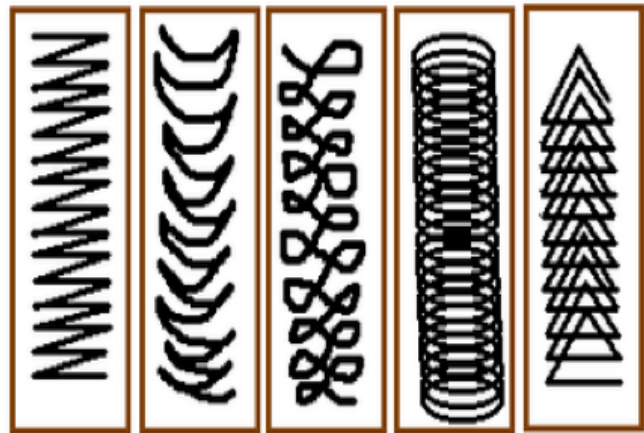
Cordones de soldadura más comunes. De izquierda a derecha. Zig-Zag, media luna, ochos, espiral y triangular.
